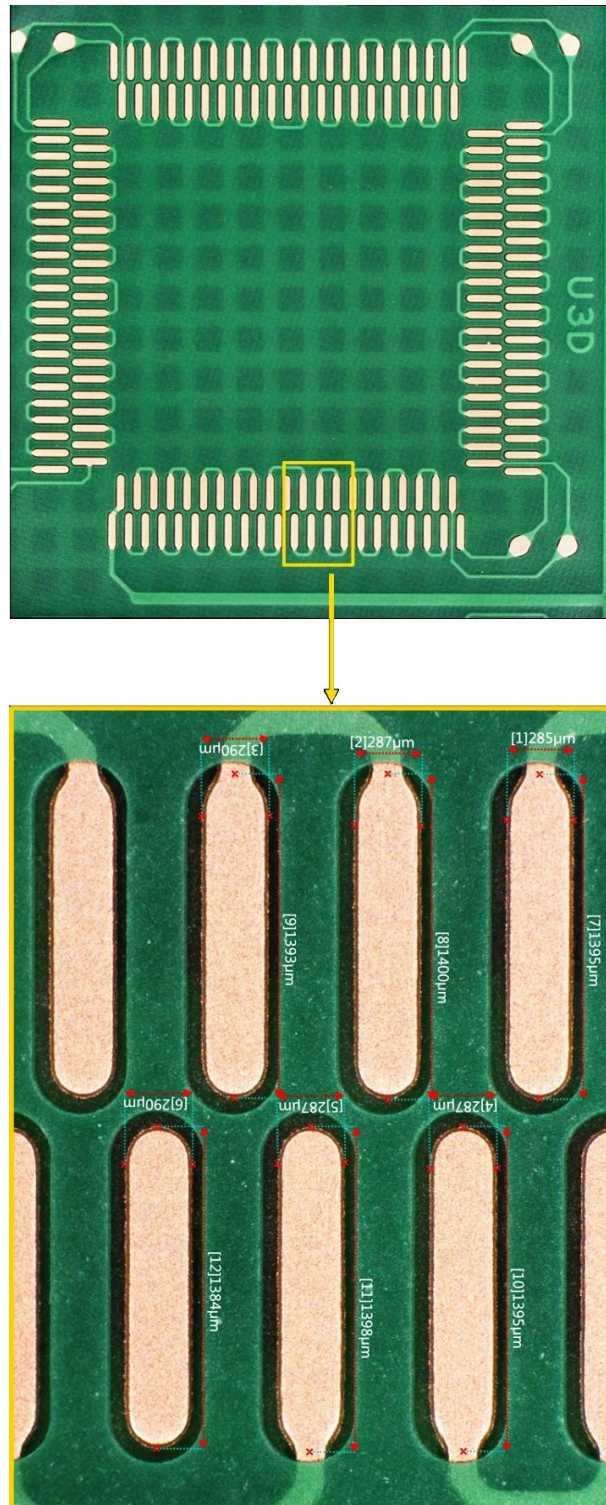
推荐的 172 MaxQFP PCB 脚印示例
